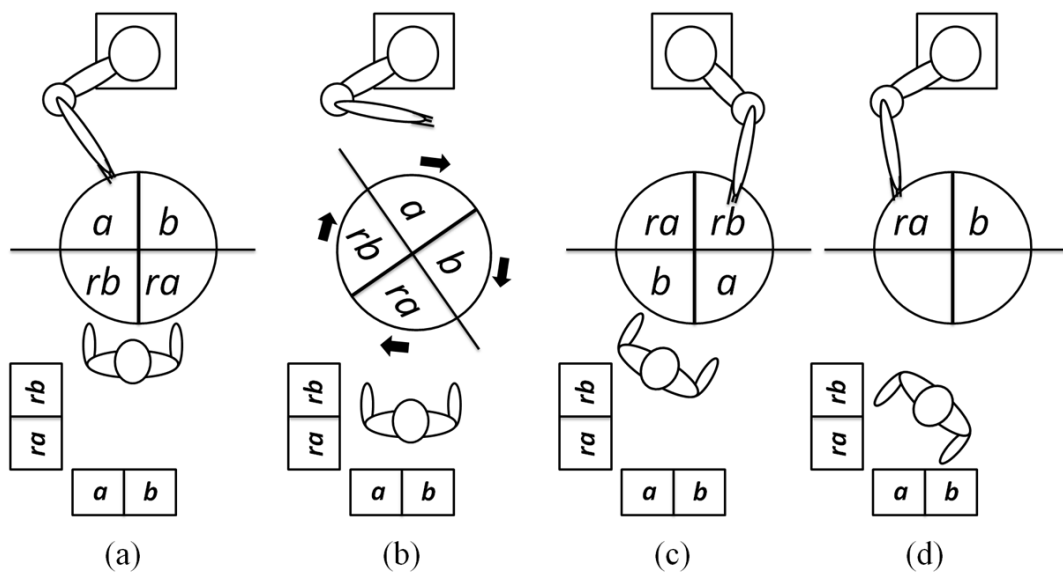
Ejemplo de la coproducción en un robot de soldadura
